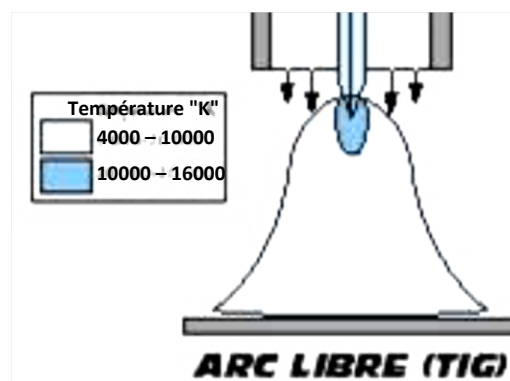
Forme de l'arc électrique de soudage TIG [5].
